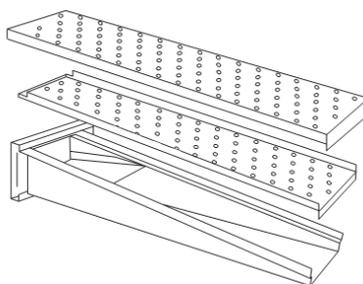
Стандартная верхняя направляющая воздуха.
